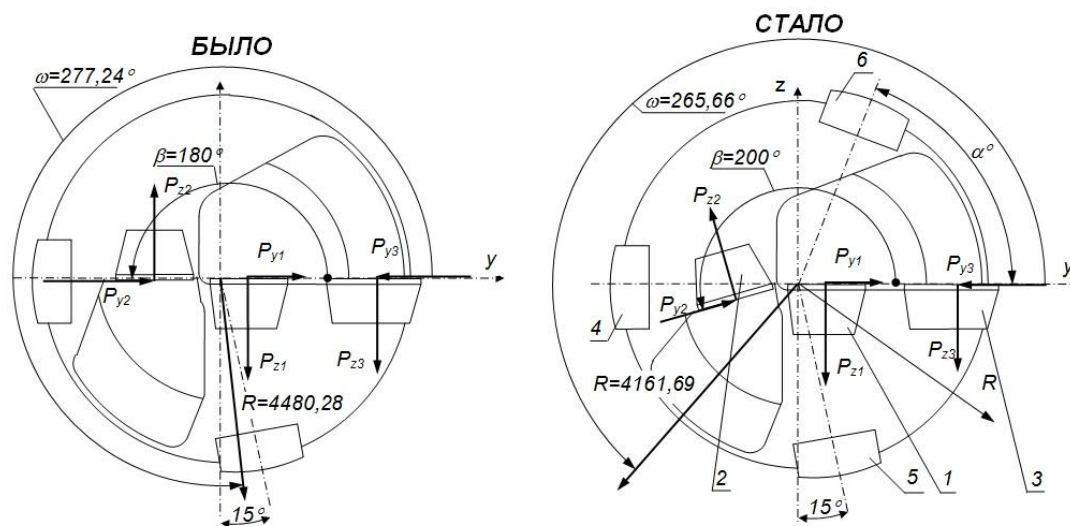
Схема новой конструкции инструмента для глубокого сверления отверстий
